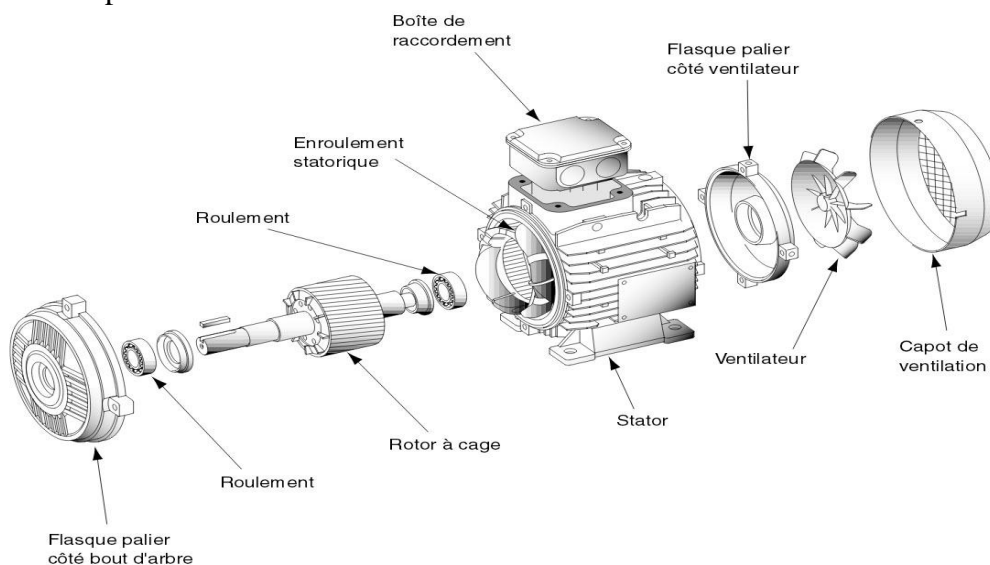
Machine asynchrone à rotor à cage d'écureuil.
